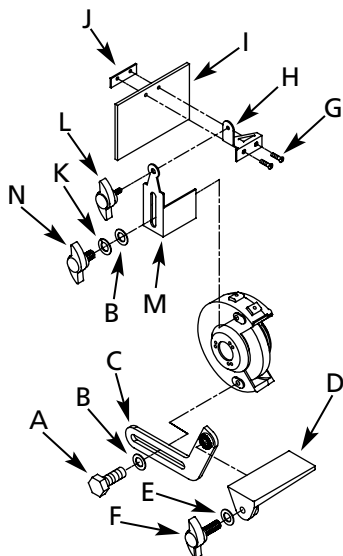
Soporte de la Herramienta Izquierdo y Conjunto de la Protección de Ojos
